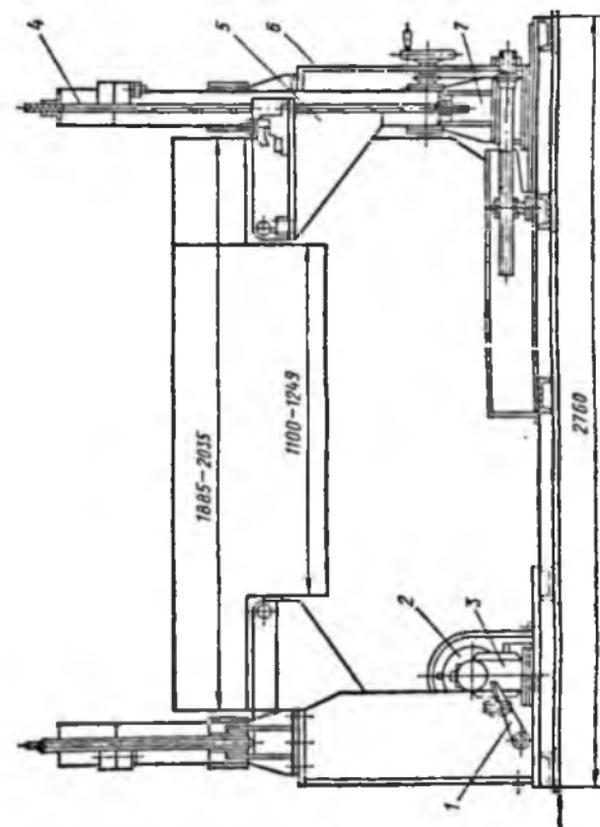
Стенд для сборки крупных деталей и сборочных единиц
